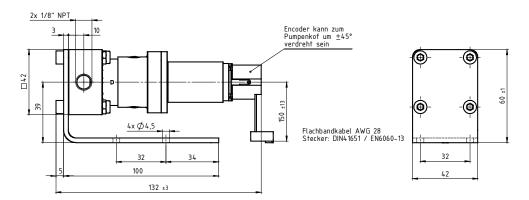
Dimensions micro annular gear pump mzr 7242 S with brushed DC motor
